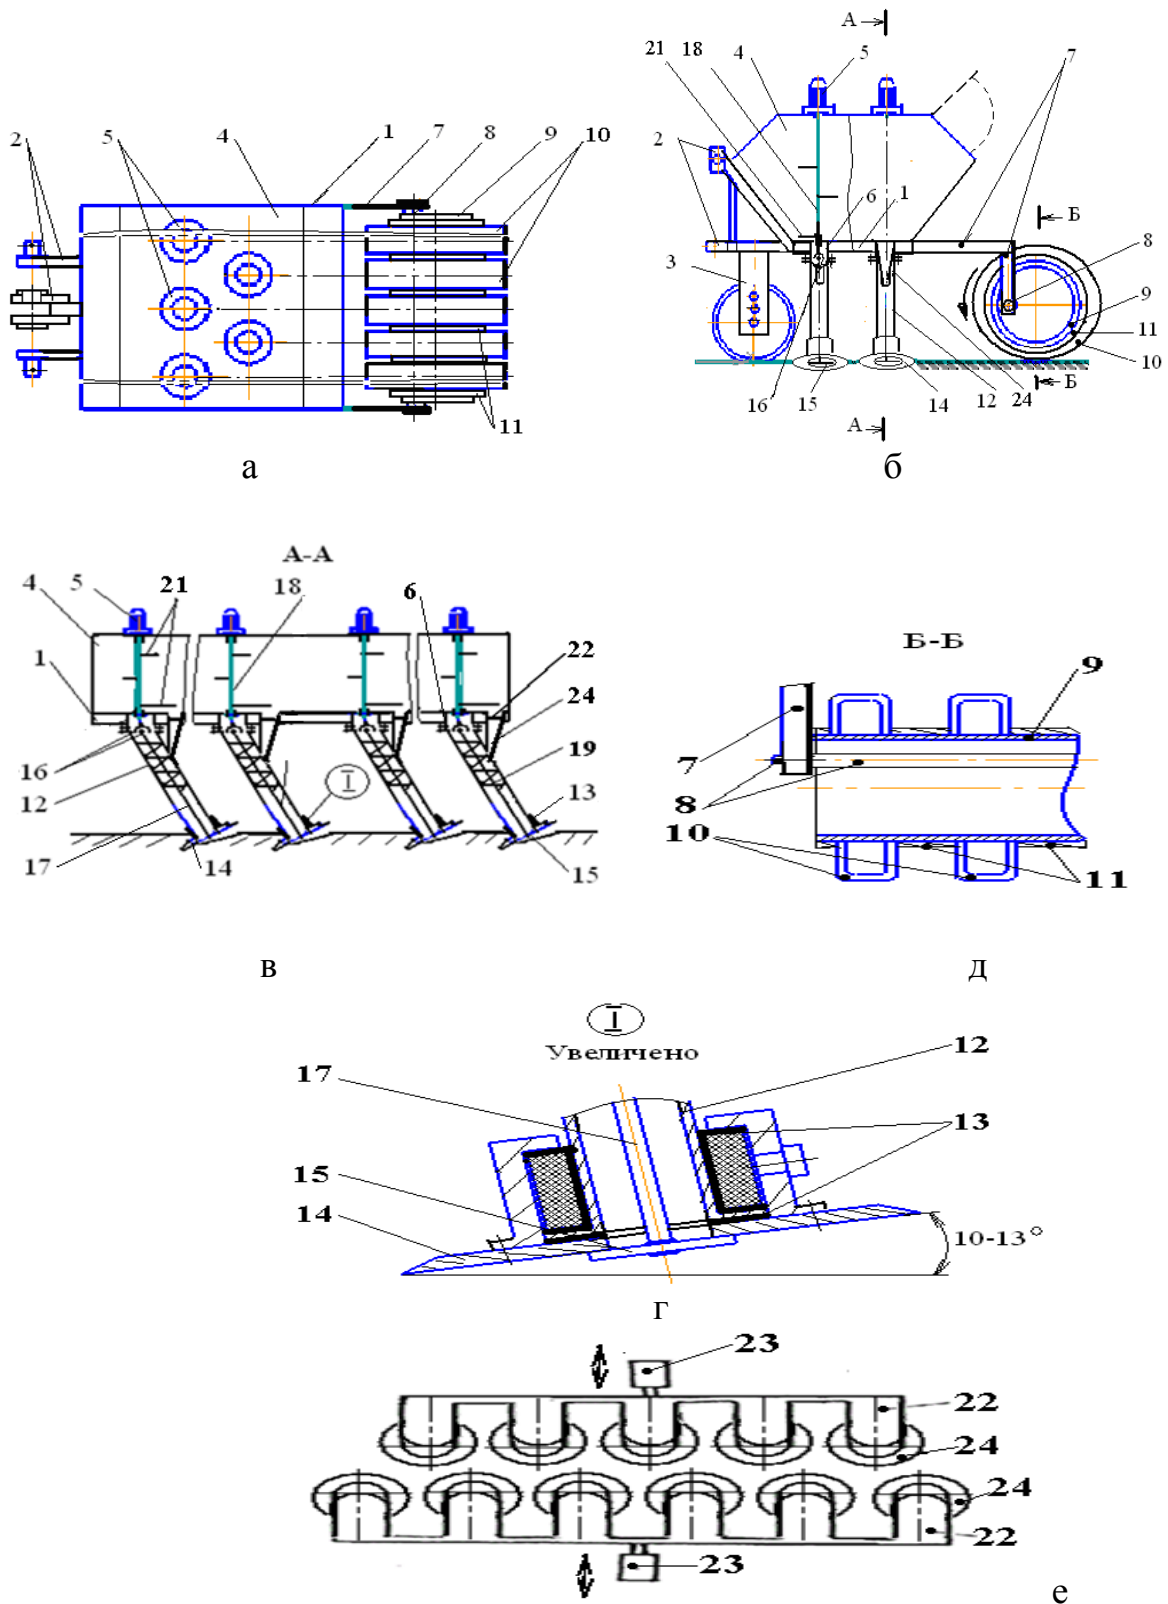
Комплекс для обработки почвы, внесения удобрений и сева семян травосмесей: а – вид сверху; б – вид сбоку; в – сечение А-А; г – увеличенный фрагмент I; д – разрез Б-Б; е – схема размещения и управления 2-х рядов дозирующих заслонок.
